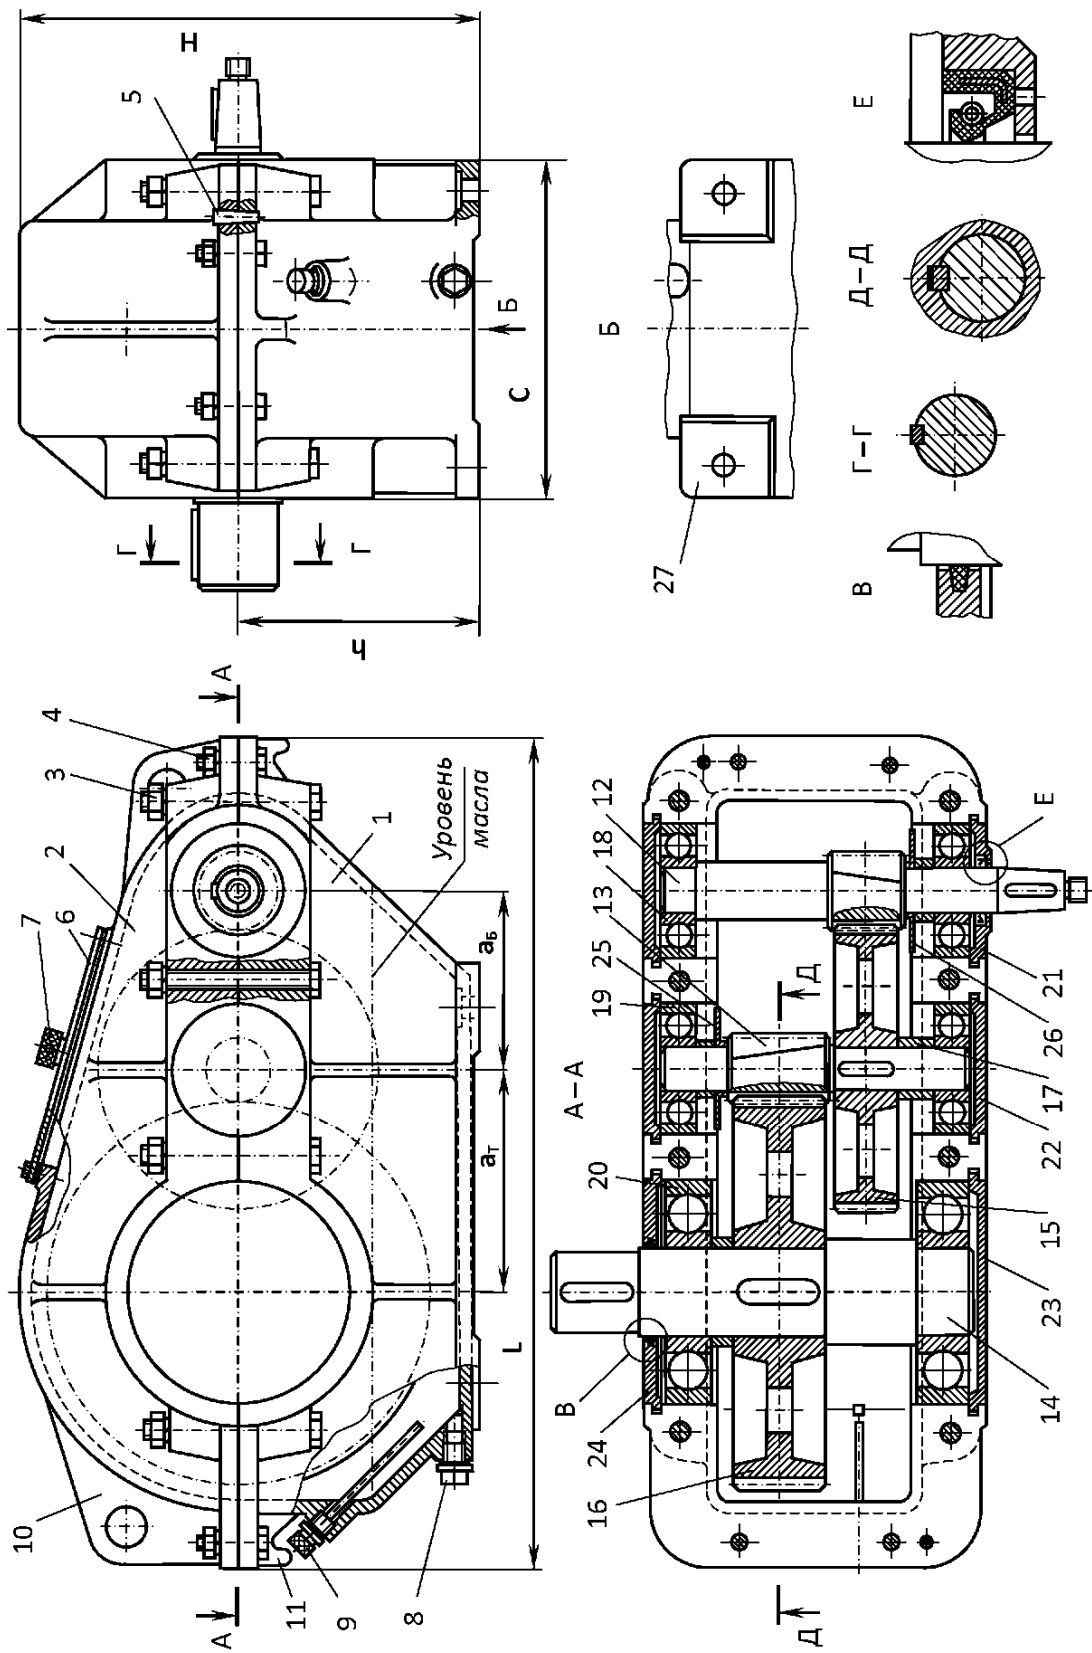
Двухступенчатый горизонтальный цилиндрический редуктор
